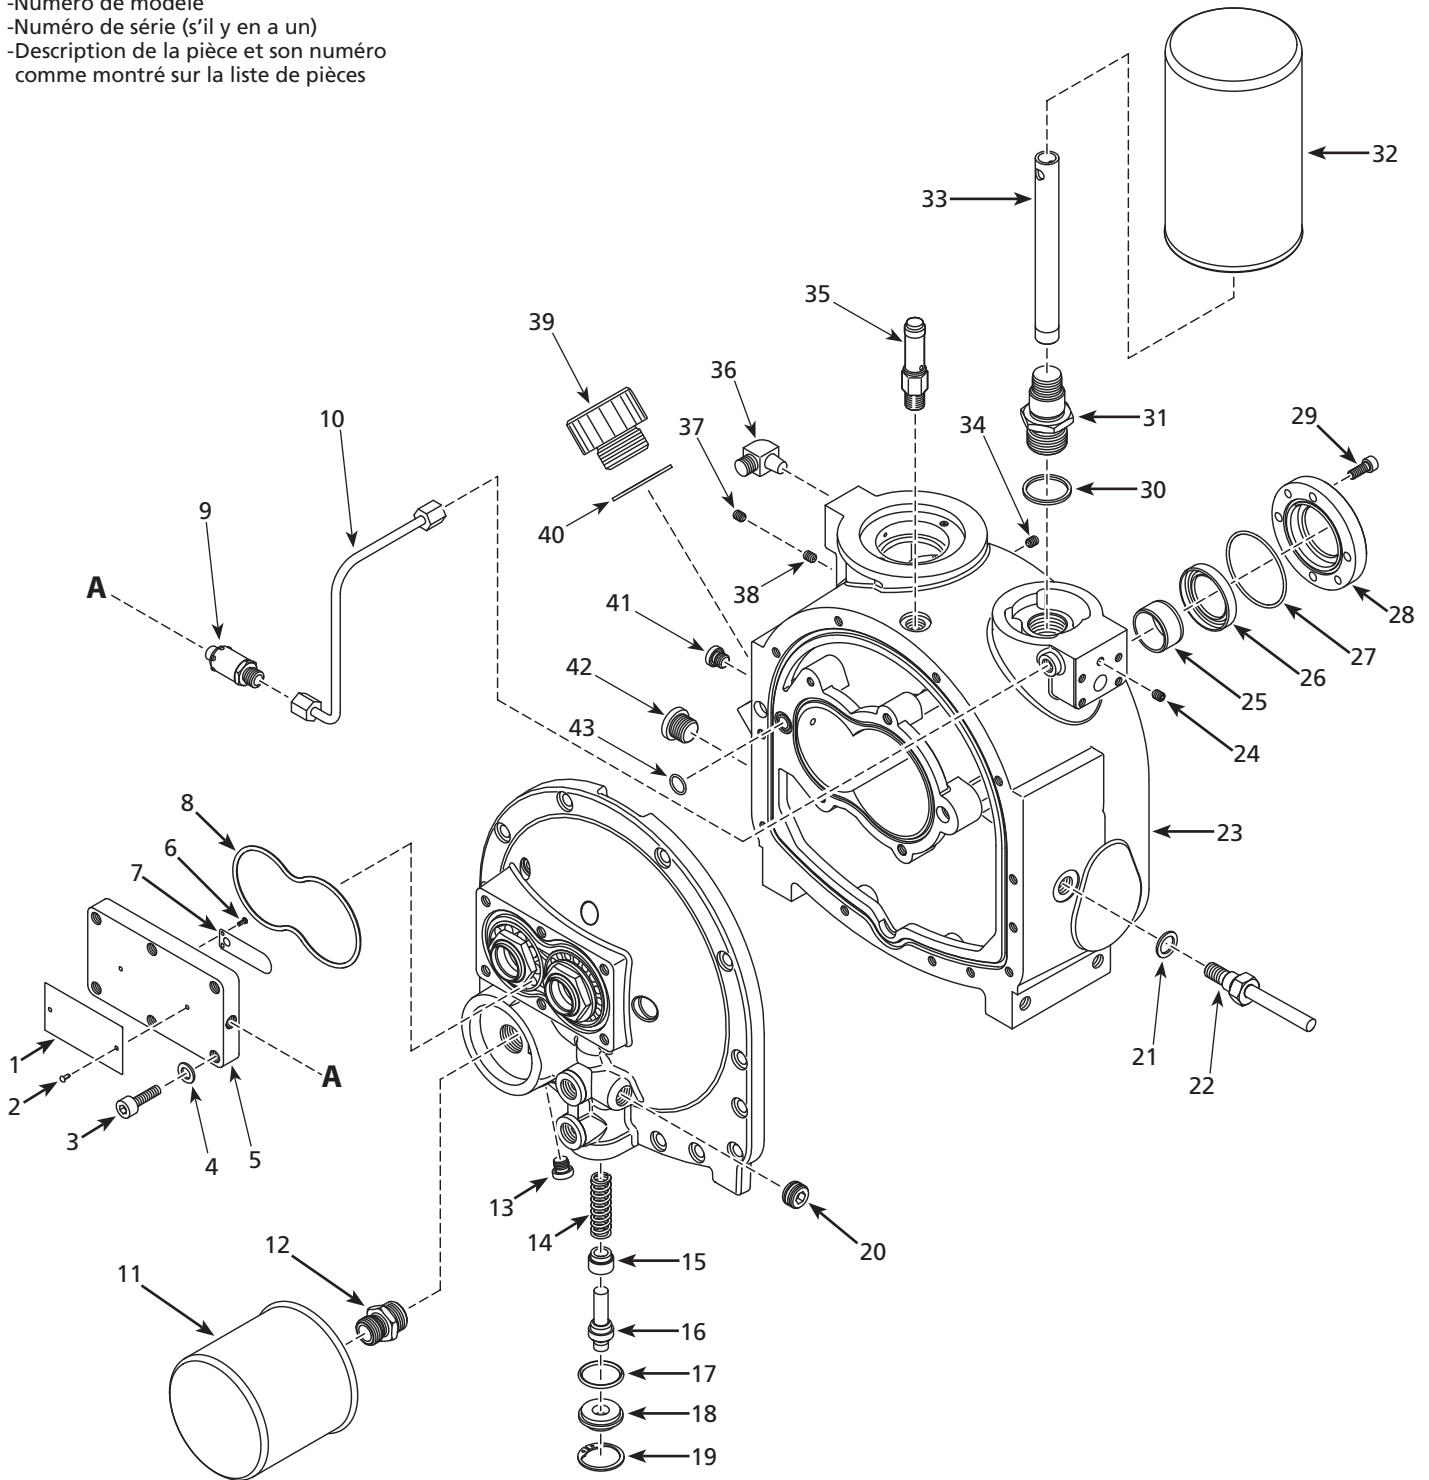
Illustration de pièces de réparation pour l'assemblage de la vis rotative de 5 à 10 HP
